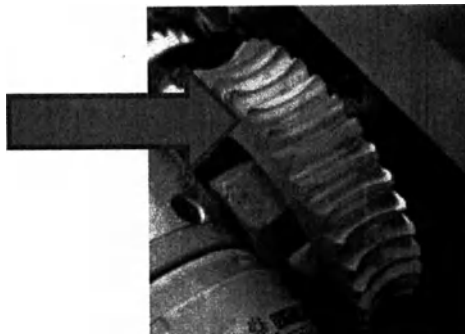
Червячное колесо редуктора подъема излучателя
